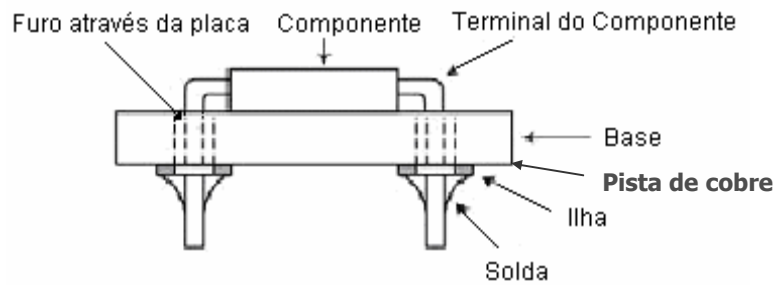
“Through-hole Technology” aplicada à montagem de componentes na placa [28].
